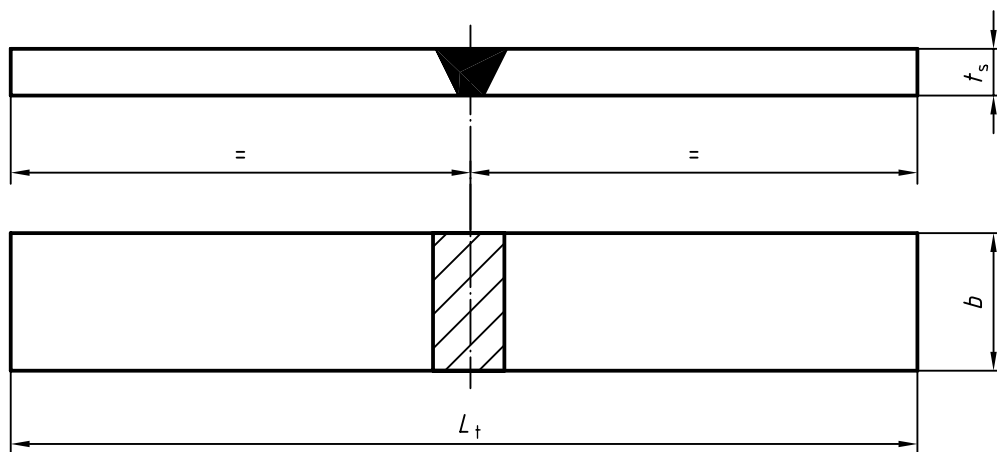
Éprouvette de pliage transversal endroit et envers sur une soudure bout à bout (RBB et FBB)
